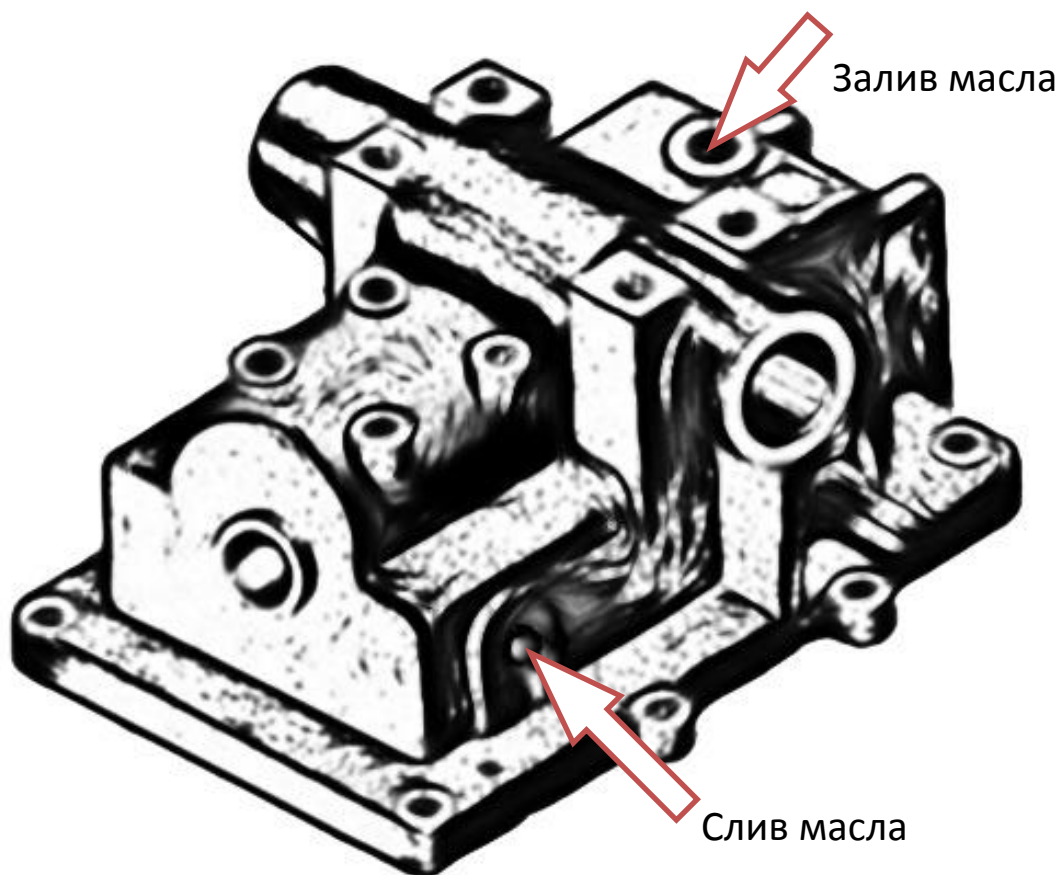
Заливное и сливное отверстия на корпусе гидробака.
